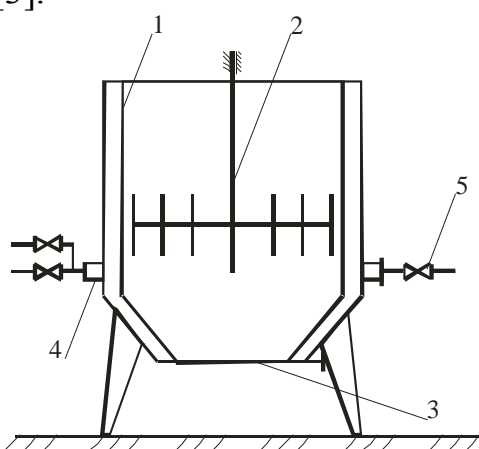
Биореактор: 1 – емкость с терморубашкой; 2 – вал с перемешивающим рабочим органом; 3 – шиберная заслонка; 4 – патрубок для подачи воды; 5 – клапан.
